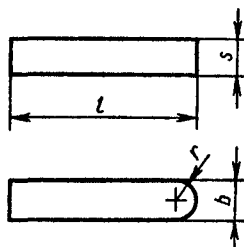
Формы напайных твердосплавных пластин для сверл
